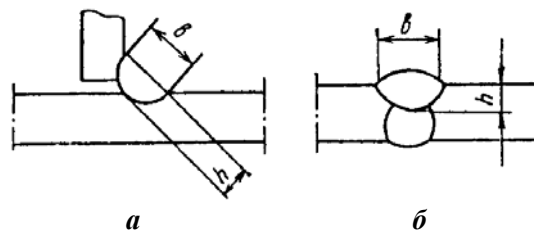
Форма провару зварних з'єднань: а – кутового шва
